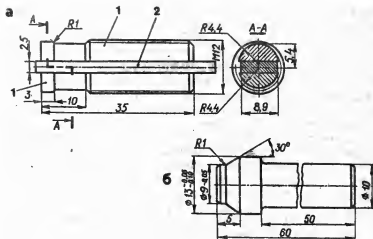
Съемник (а) для распылителя и оправка (б) для его запрессовки:
